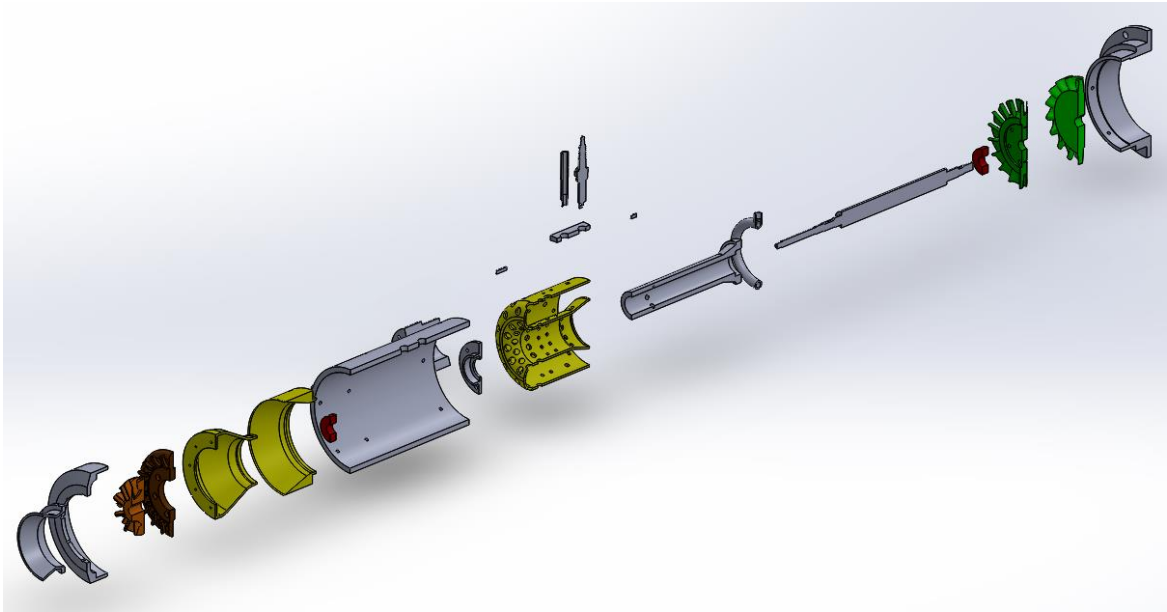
Vista explosionada de los componentes de la micro turbina a gas.
